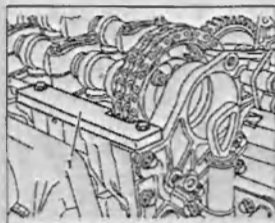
Установите блокировочное приспособление 1 на головку блока цилиндров.
